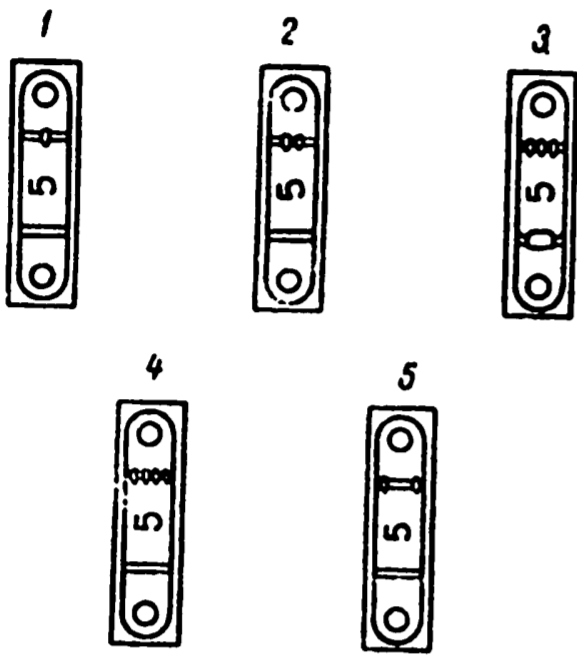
Метки на крышках коренных подшипников (счет опор ведется от передней части двигателя) и условный номер блока цилиндров
